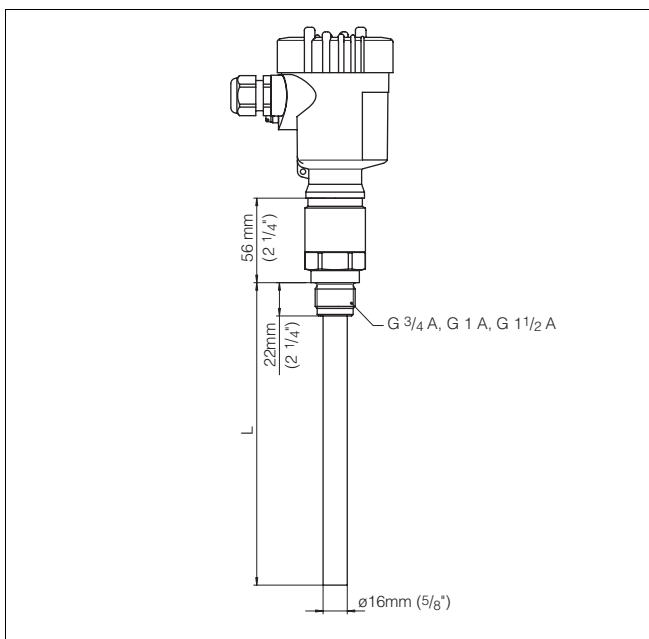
VEGACAP 64 с резьбовым присоединением G1A
